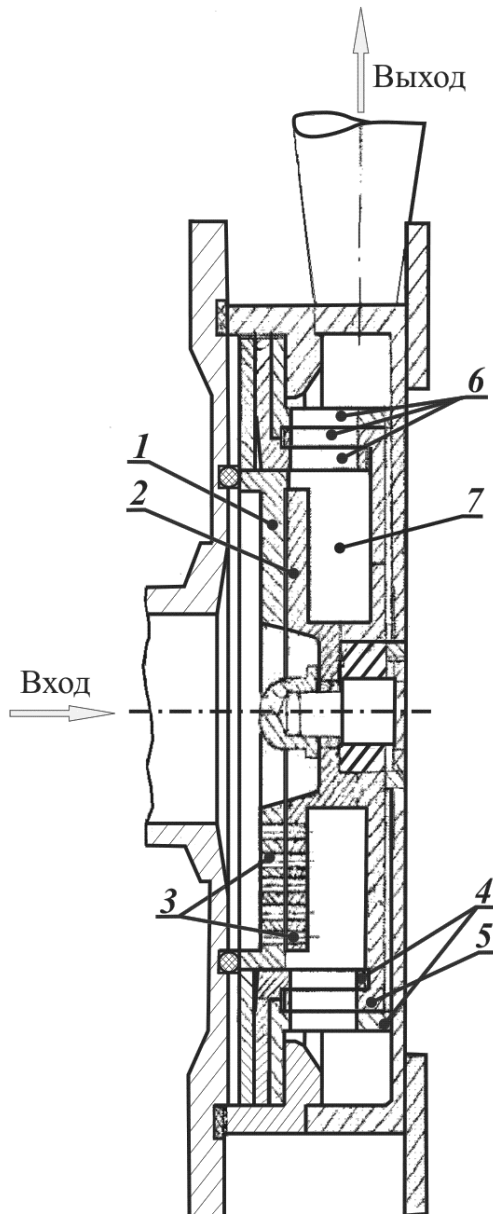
Схема конструкции дисково-цилиндрического аппарата:
